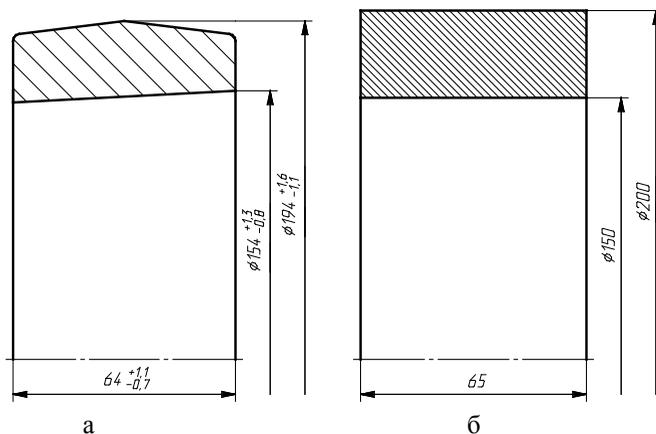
Заготовка: а – на ГКМ; б – из трубы ГОСТ8732-78
